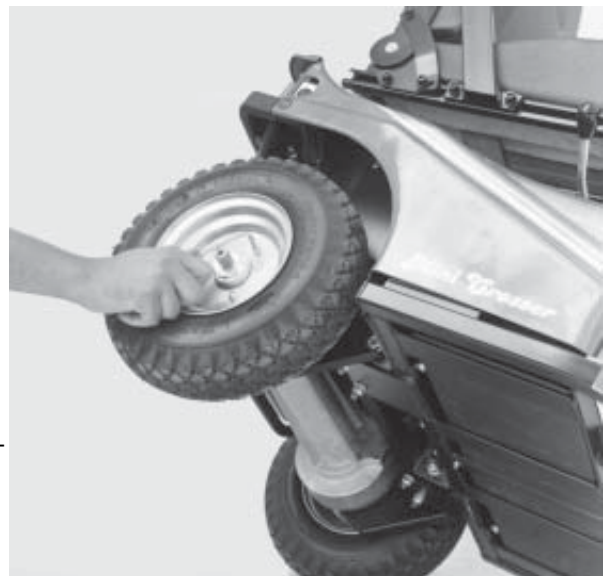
Auf dieser Abb. sind die drei Schrauben zu sehen, die entfernt werden müssen. Danach kann das Rad abgenommen werden. Beim Wiedereinsetzen müssen die Federscheiben zwischen der Radfelge und Schraube angebracht werden. Schrauben gut anziehen.
